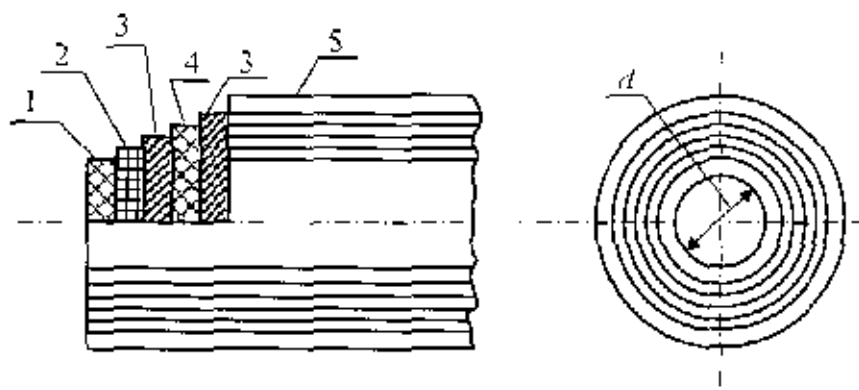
Схема конструкции рукава высокого давления: 1 — внутренний резиновый слой; 2 — хлопчатобумажная оплетка; 3 — металлическая оплетка; 4 — промежуточный резиновый слой; 5 — наружный резиновый слой
